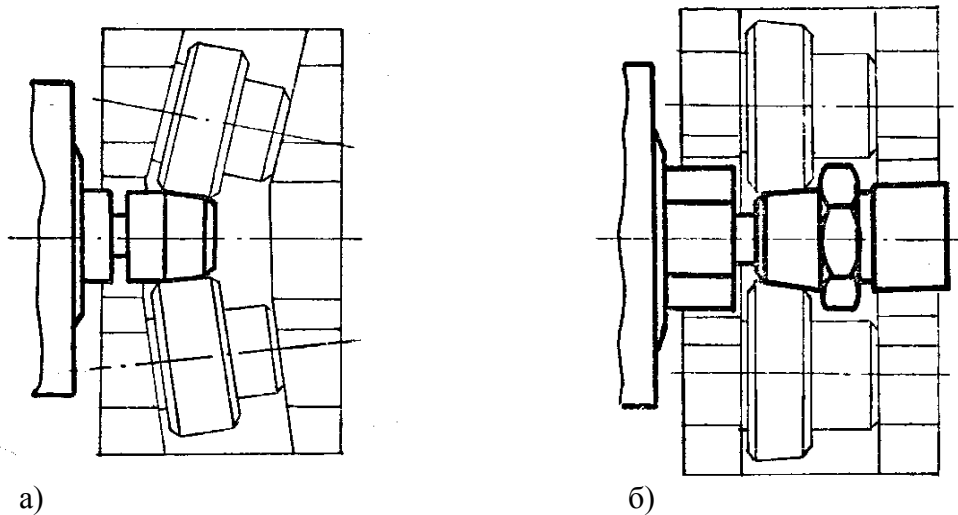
Резьбонакатные головки для накатывания конической резьбы: а- с двумя цилиндрическими роликами; б- с двумя коническими роликами.
